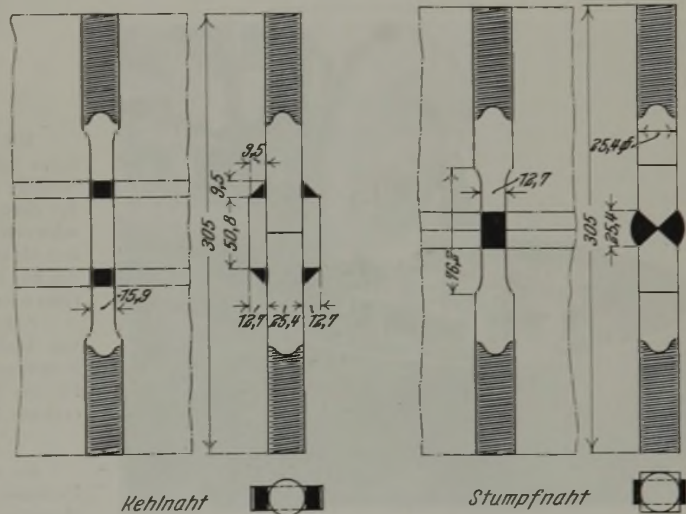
und 4. Probenformen der Schweißverbindungen für die Dauerfestigkeitsprüfung.
